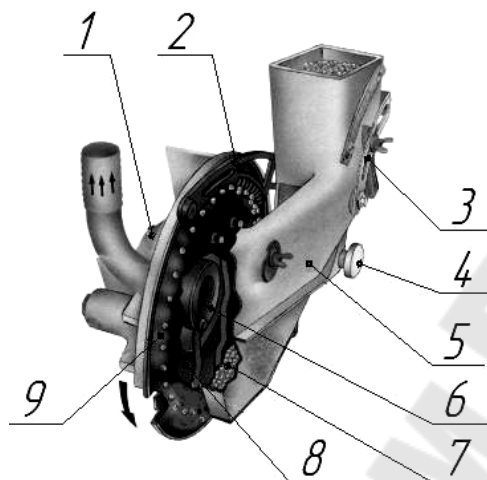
Высевующий аппарат: 1 – корпус сборный; 2 – отсекаатель; 3 – указатель положения отсекаателя; 4 – винт; 5 – полукорпус с горловиной; 6 – обойма; 7 – камера зерновая; 8 – камера вакуумная; 9 – диск высевующий
